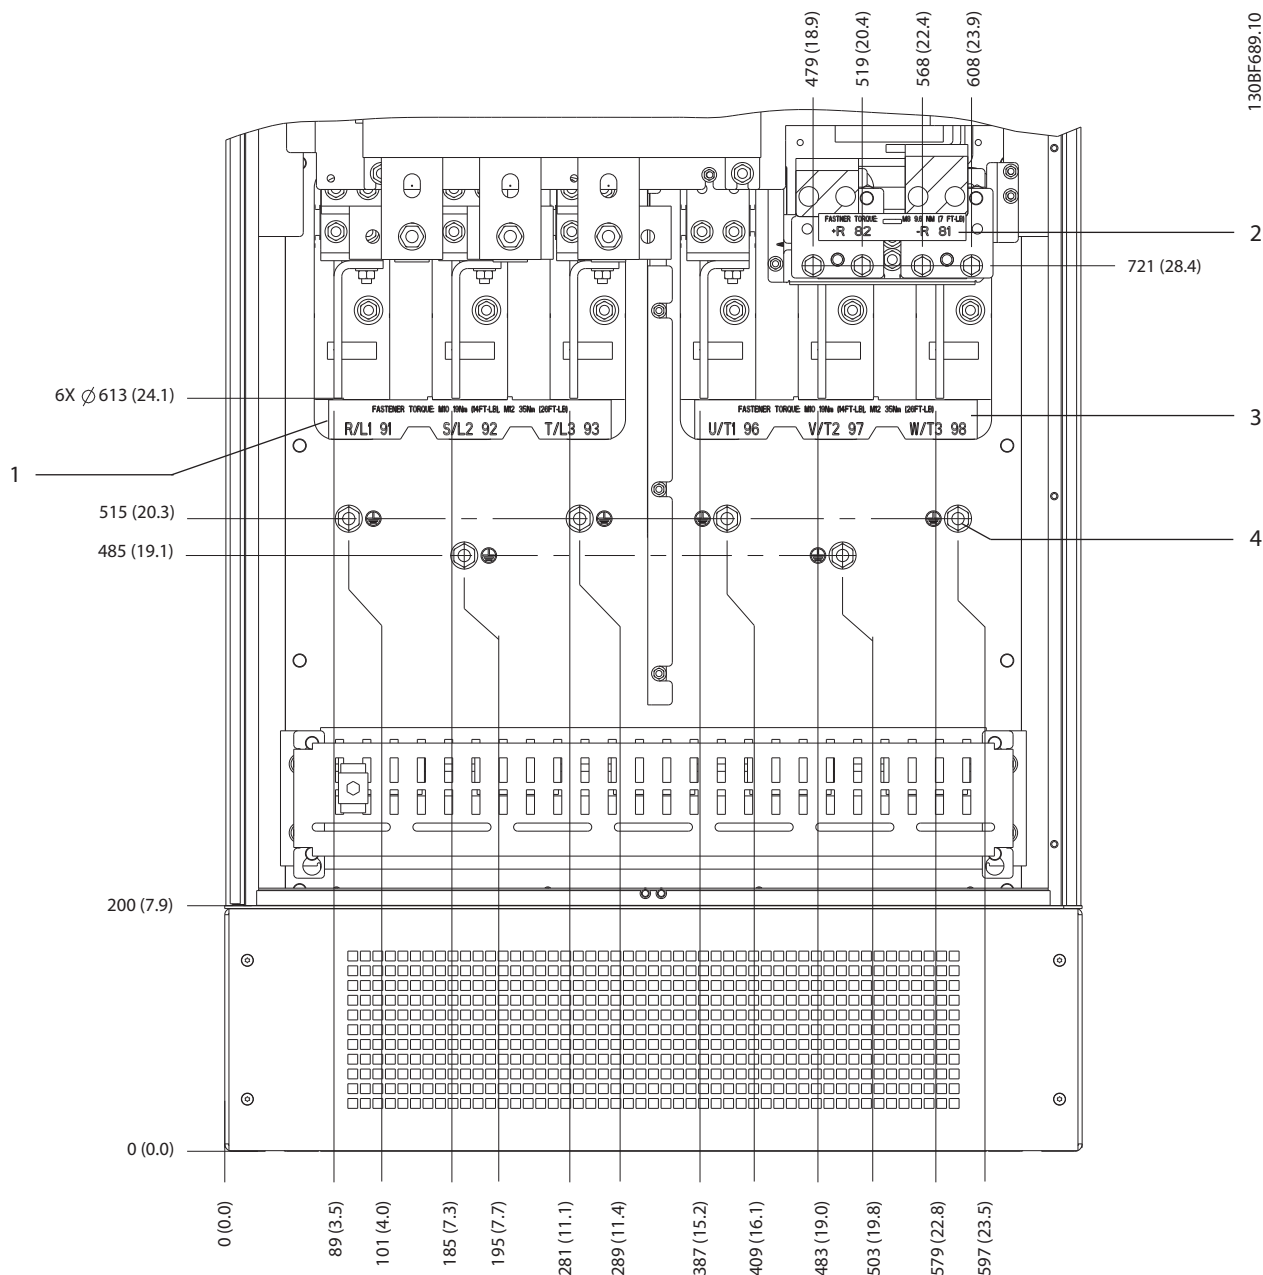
Dimensões do Terminal E1h (vista frontal)
